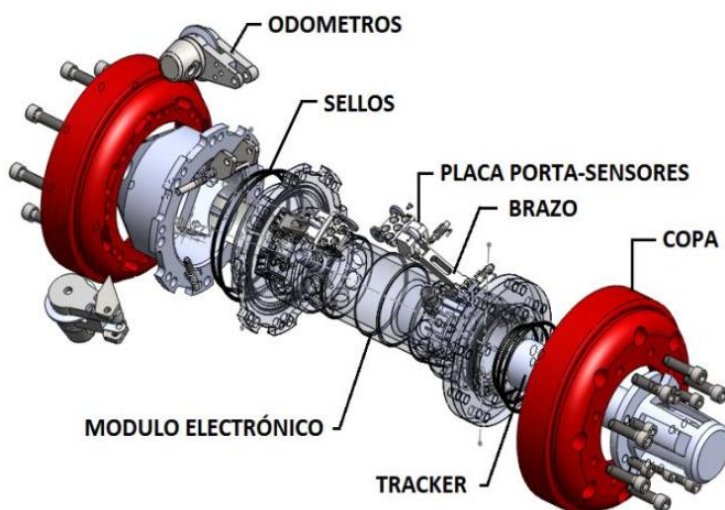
Componentes principales del equipo instrumentado desarrollado por [6].
